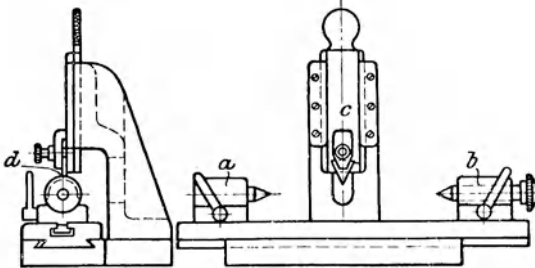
Messung des Flankenwinkels von Gewinden mittels Dreiecks.
